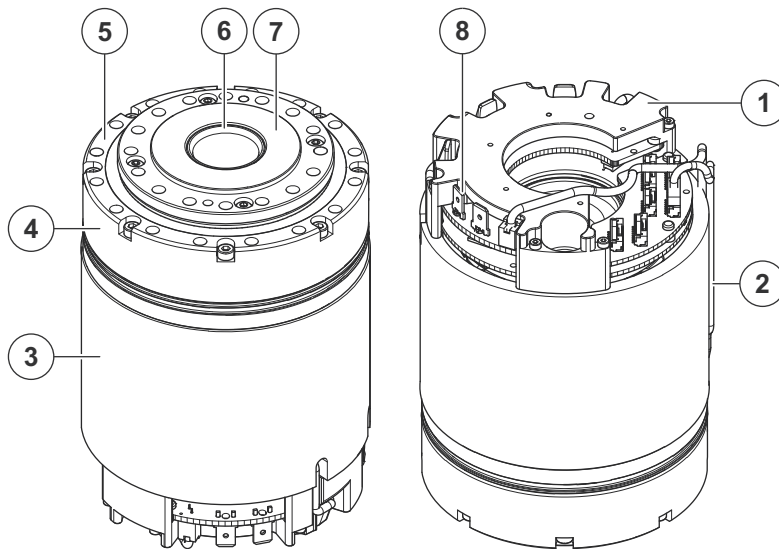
Hauptbaugruppen TUAKE DRIVE (Beispielabbildung)
